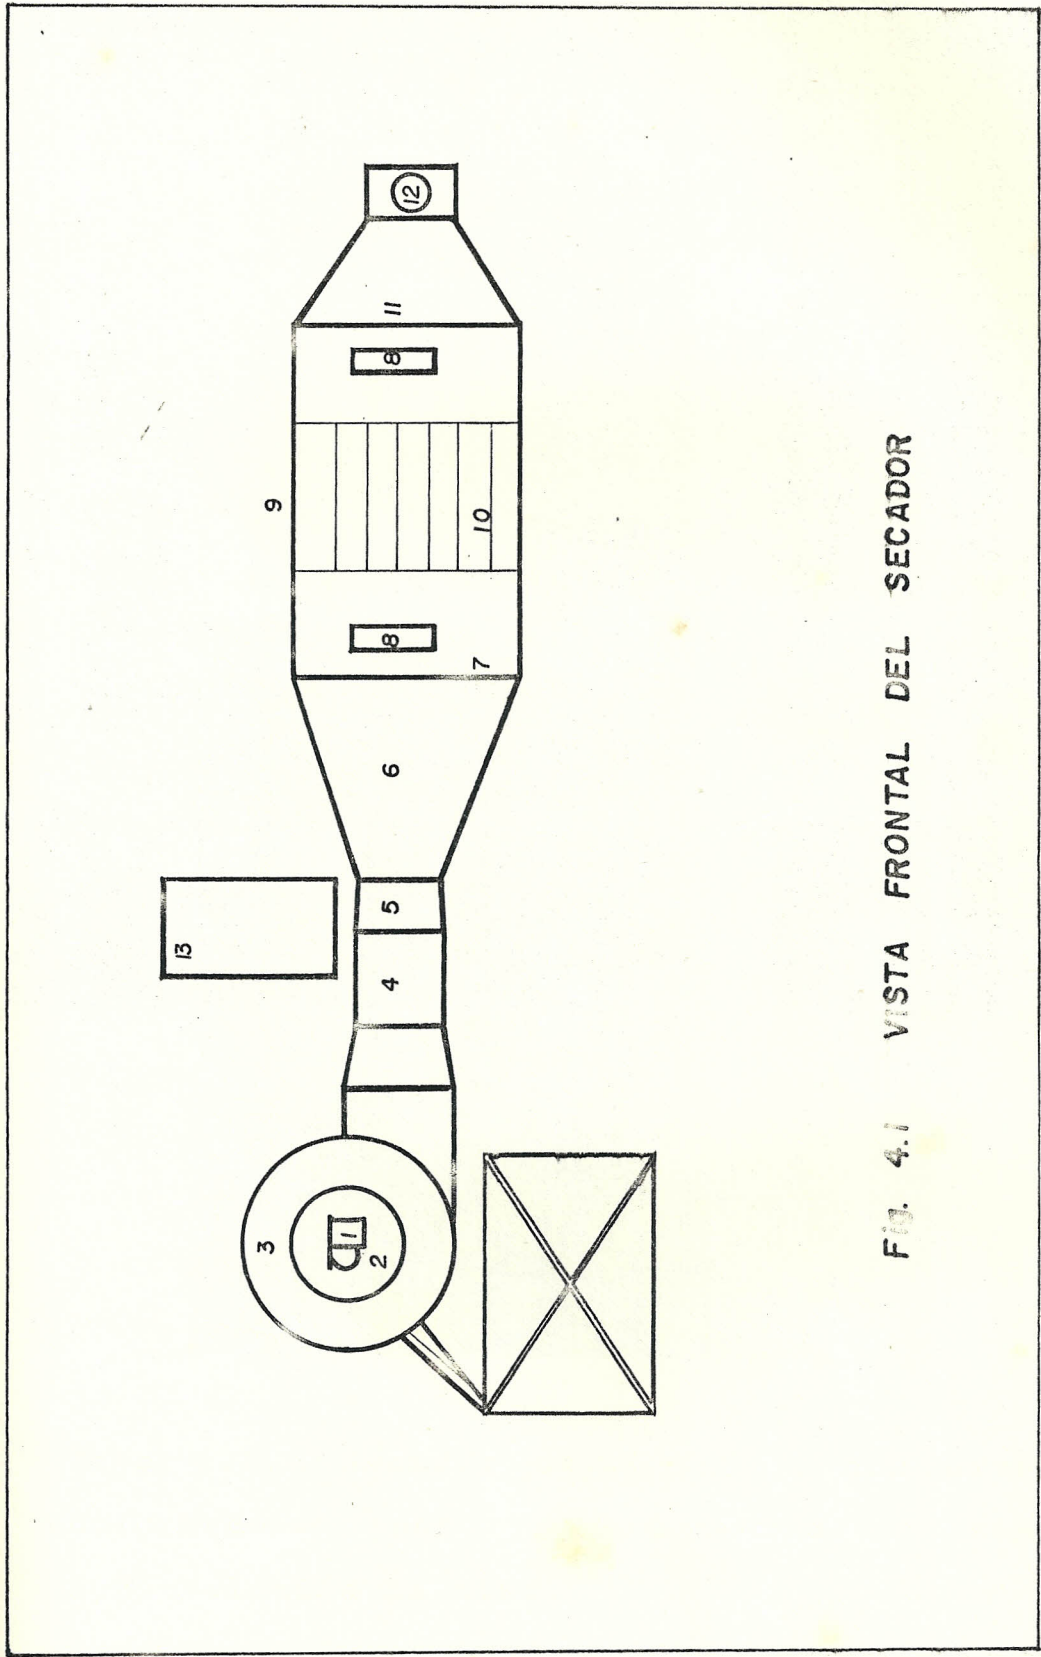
VISTA FRONTAL DEL SECADOR
